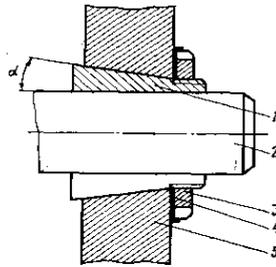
Безшпонкове з'єднання конічними розрізними втулками спряження вал — зірочка
